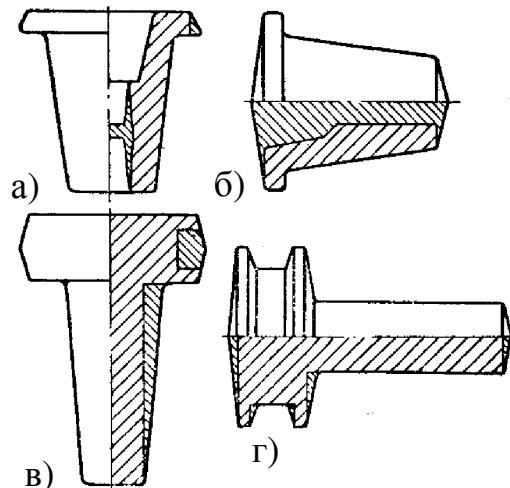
Вплив поверхні роз’єднання штампа на форму поковок
